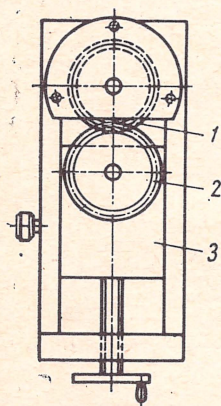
Приспособление для безопасной зачистки заусенцев на зубьях зубчатых колес
